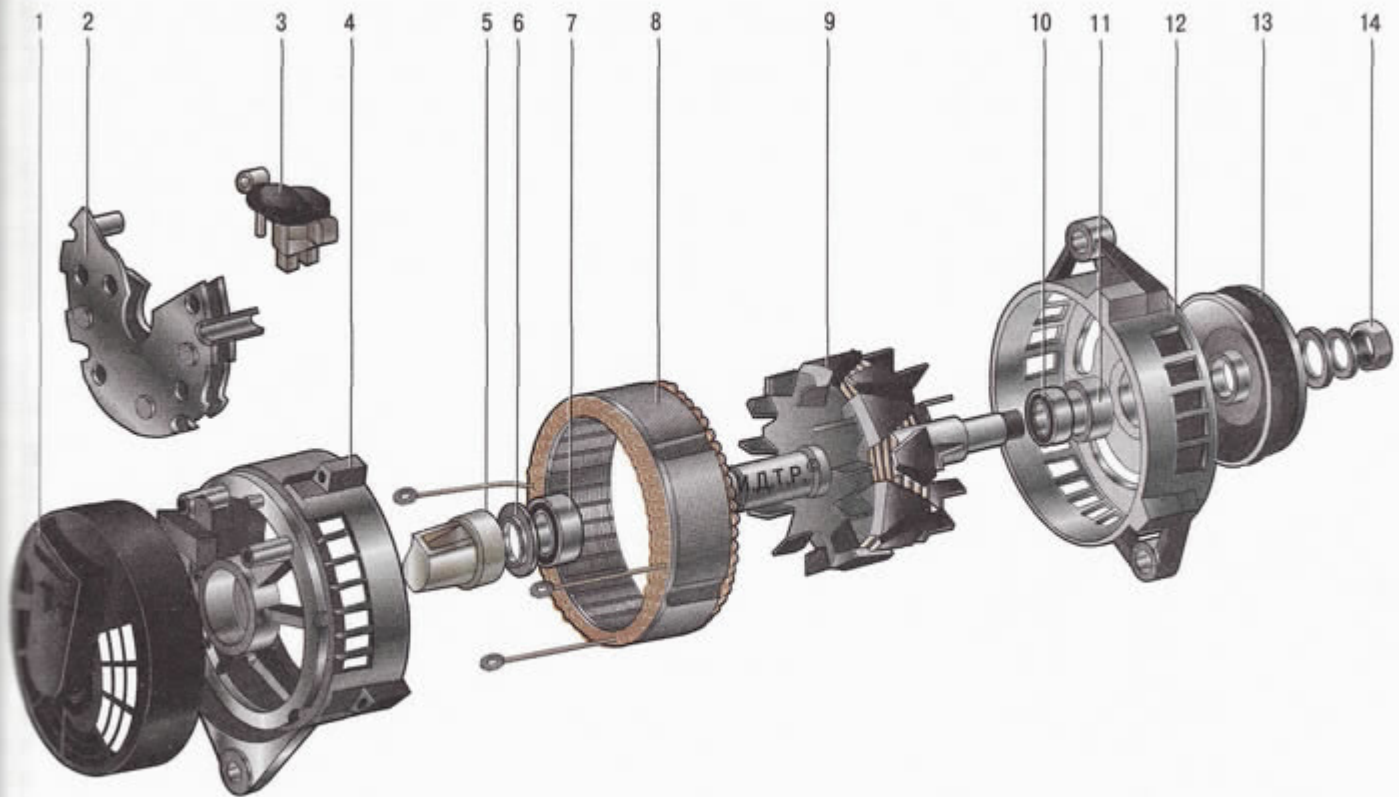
Детали генератора 97.3701: 1 – кожух; 2 – выпрямительный блок; 3 – регулятор напряжения со щеткодержателем; 4 – крышка со стороны контактных колец; 5 – втулка; 6 – шайба; 7, 11 – подшипники; 8 – статор; 9 – ротор; 10 – дистанционная втулка; 12 – крышка со стороны привода; 13 – шкив; 14 – болт крепления шкива
